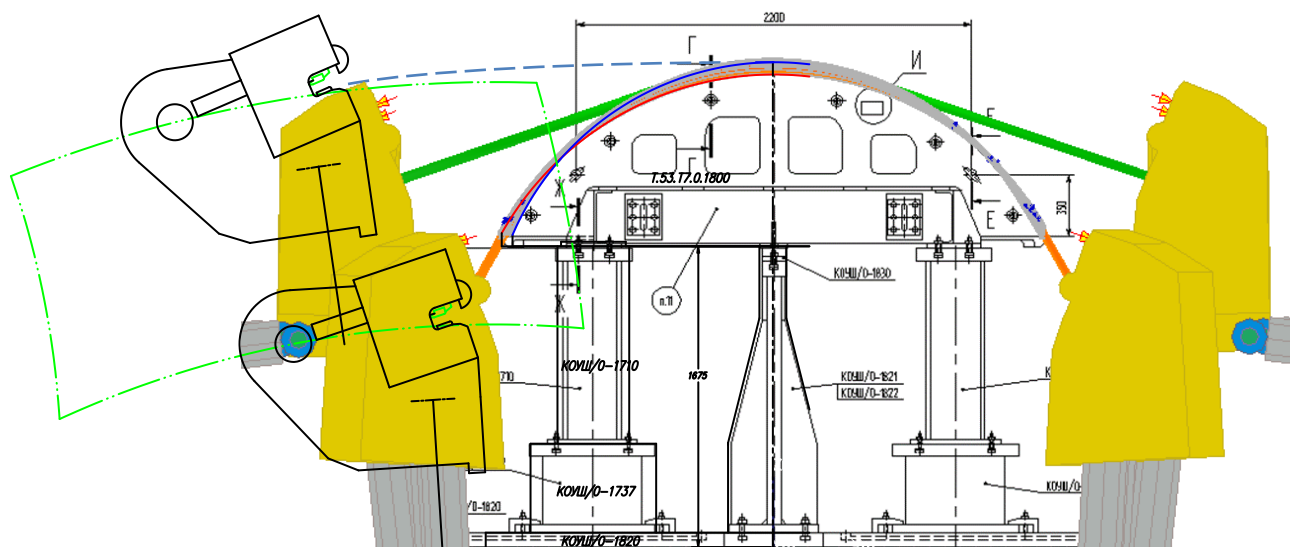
Схема обтяжки крупногабаритной заготовки на пределе кинематических возможностей
